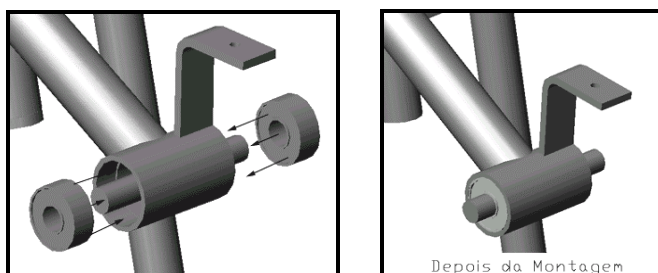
Soldagem dos eixos traseiros no tubo de 28 mm.
